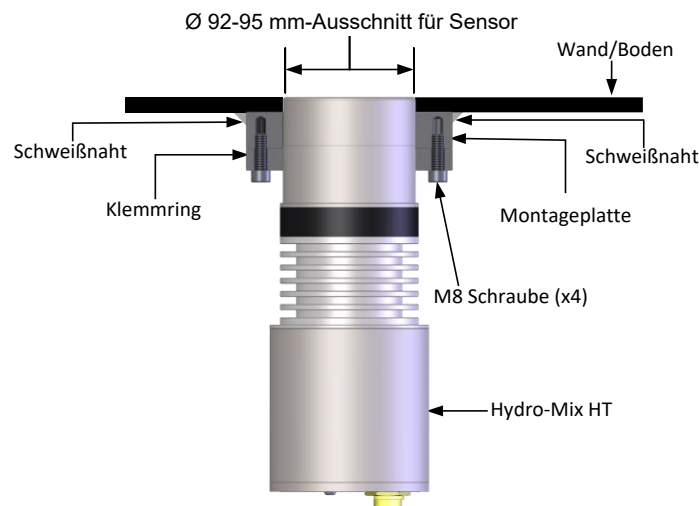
Einbau des Sensors (Extern montierte Montageplatte)
